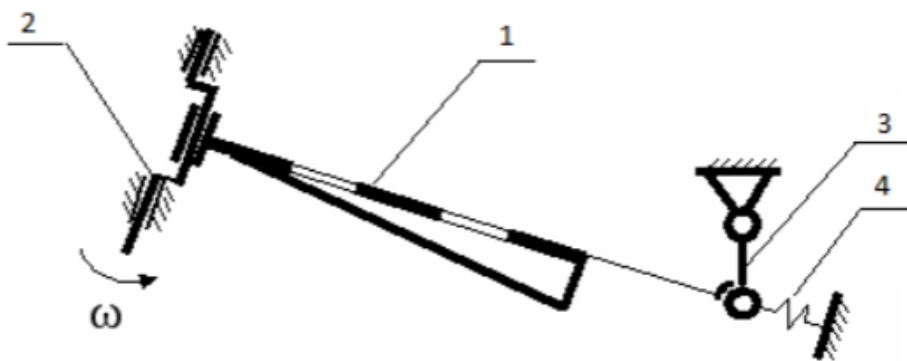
Схема привода решета от коленчатого вала: 1 - решето; 2 - коленчатый вал; 3 - подвес; 4 - пружина
